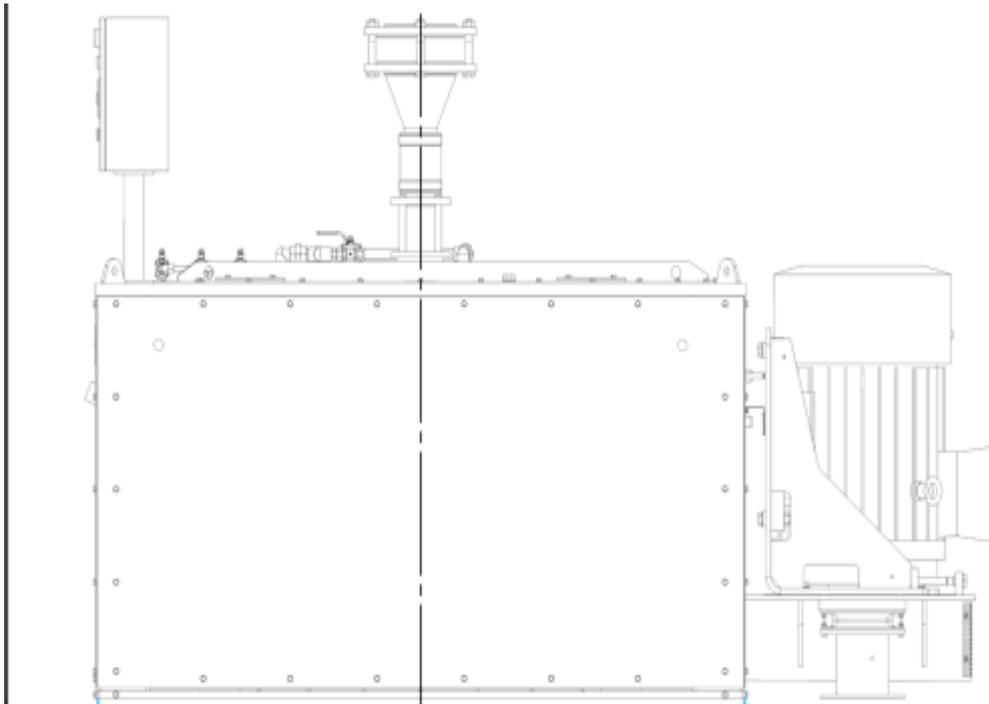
Dessin de la centrifugeuse BMA k2300
